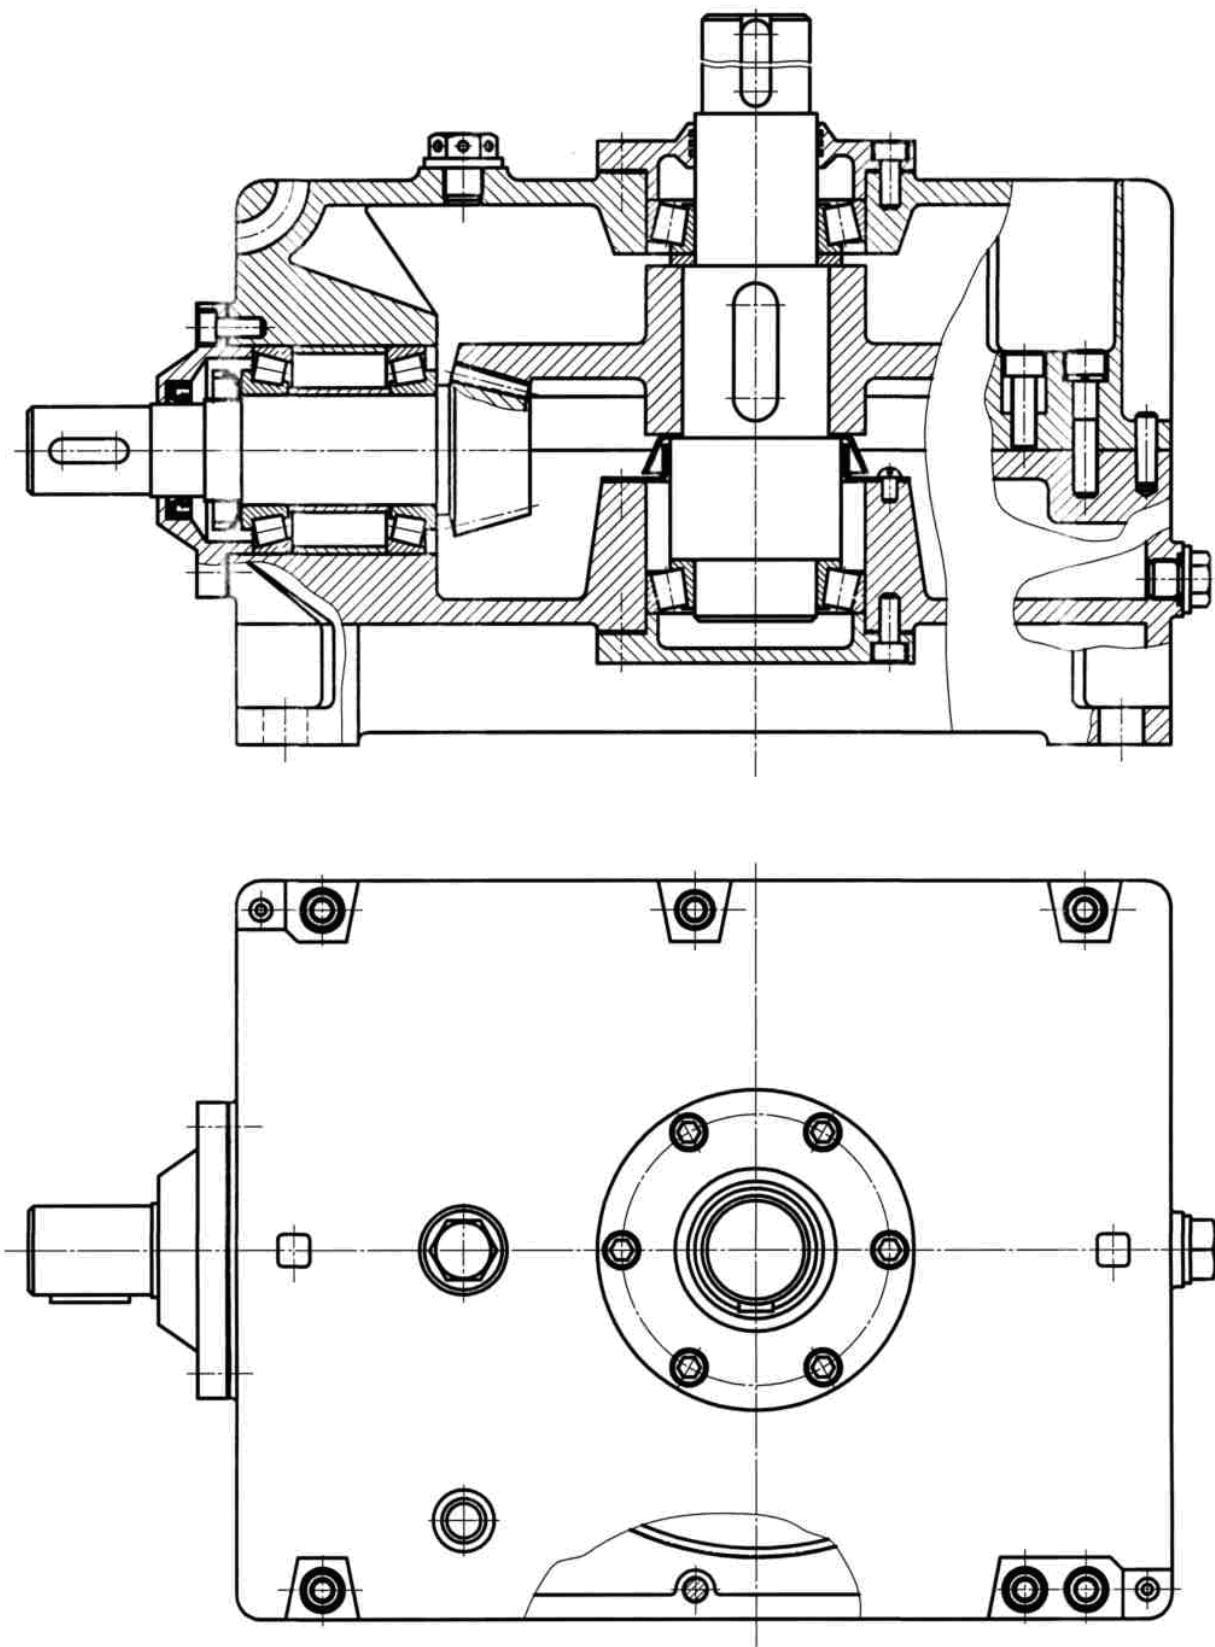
Редуктор конический с вертикальным тихоходным валом
